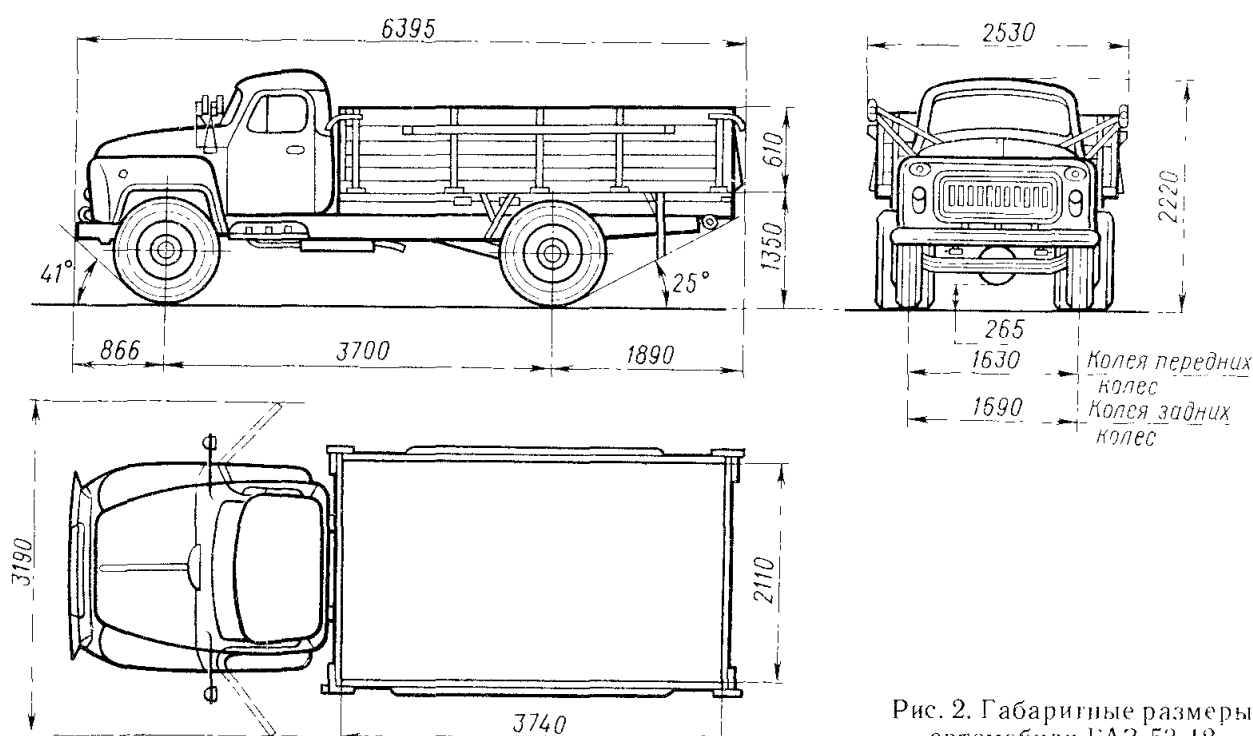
Габаритные размеры автомобиля ГАЗ-53-12
